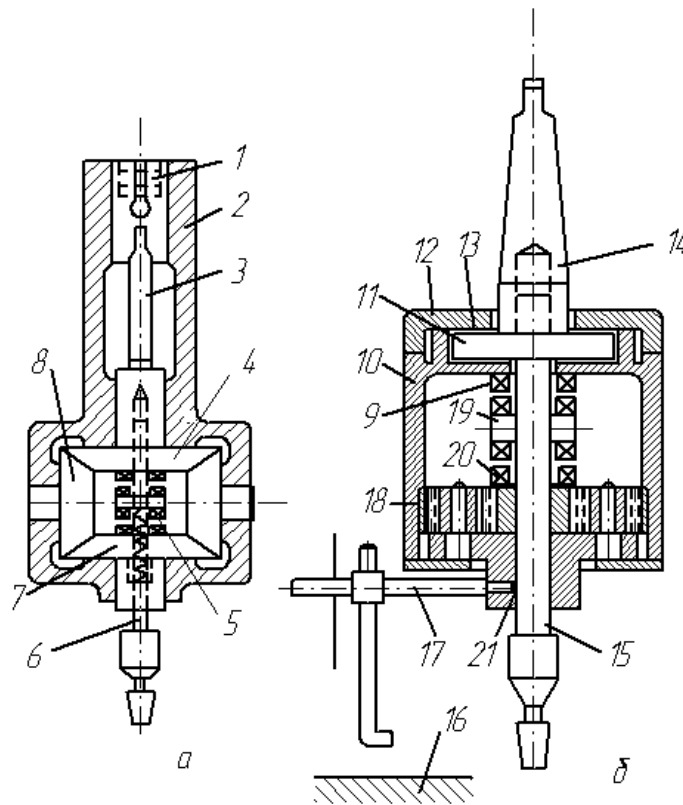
Реверсивні головки для нарізування різьблення мітчиками
